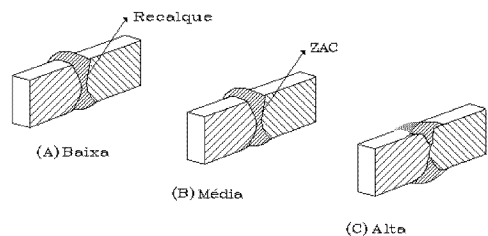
Efeito da Pressão Axial sobre a Geometria da Junta na Soldagem por Inércia.
